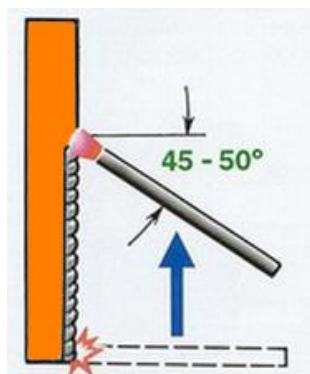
Тип шва – С2, сварка ручная дуговая ГОСТ 5264-80, положение шва – вертикальное; толщина металла – 4 мм.
